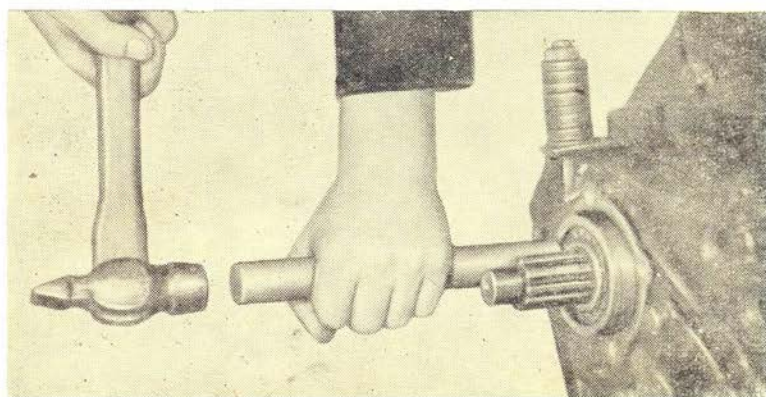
Запрессовка в картер заднего подшипника в сборе с ведущим валом
